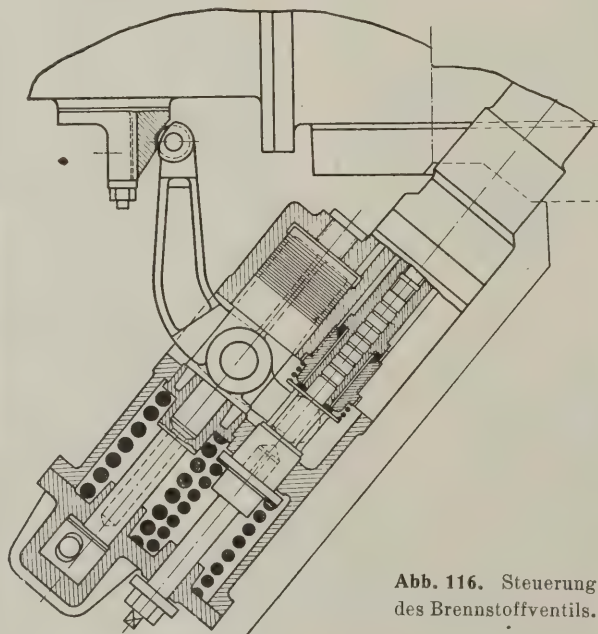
bis 116. Teile der MacLagan-Maschine.
